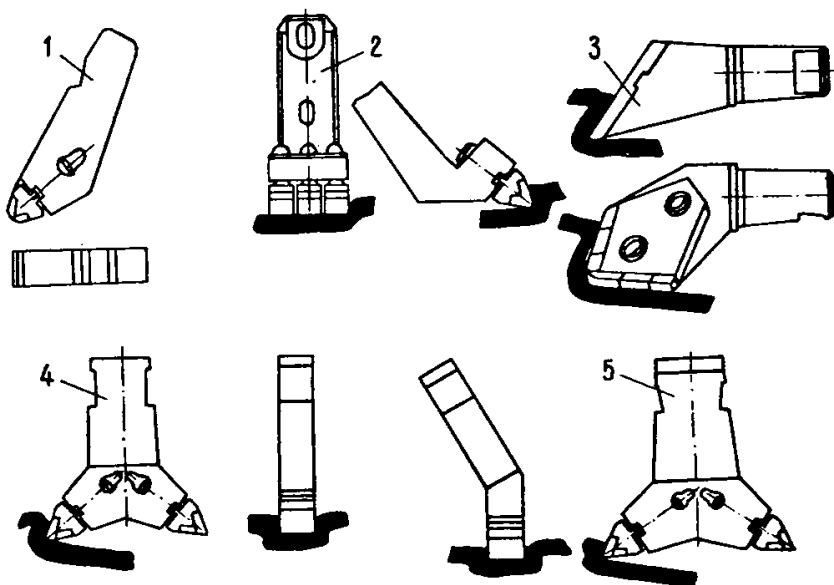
Резцы и ножи для струга УСТ-2А:
